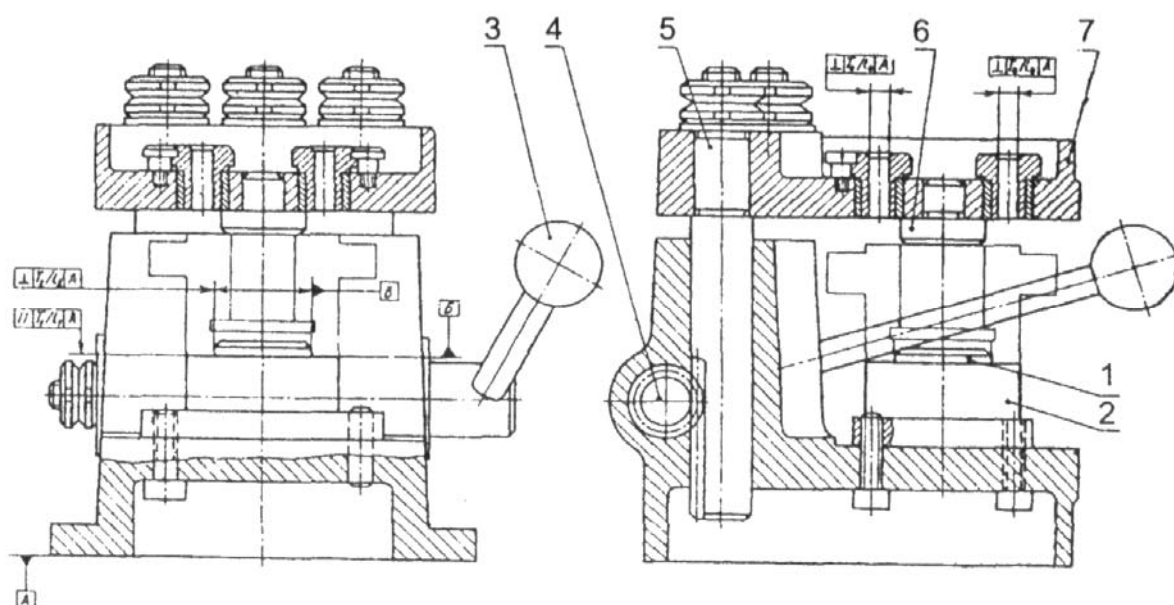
Наладка скальчатого кондуктора для сверления отверстий во втулке
